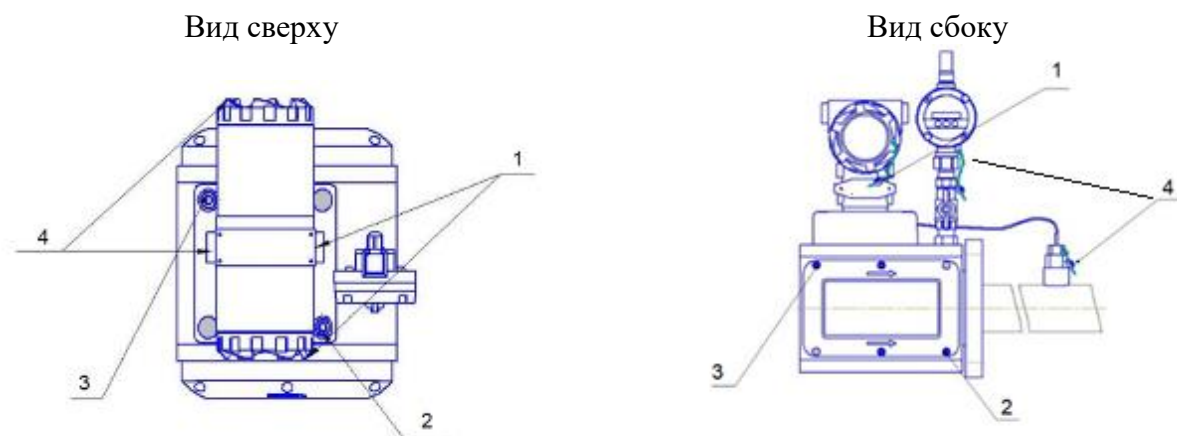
Корпус прямоугольного сечения с совмещенными защитными крышками
